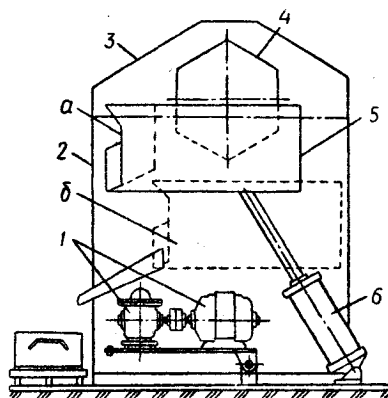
Установка для миття дрібних деталей в обертовому барабані
